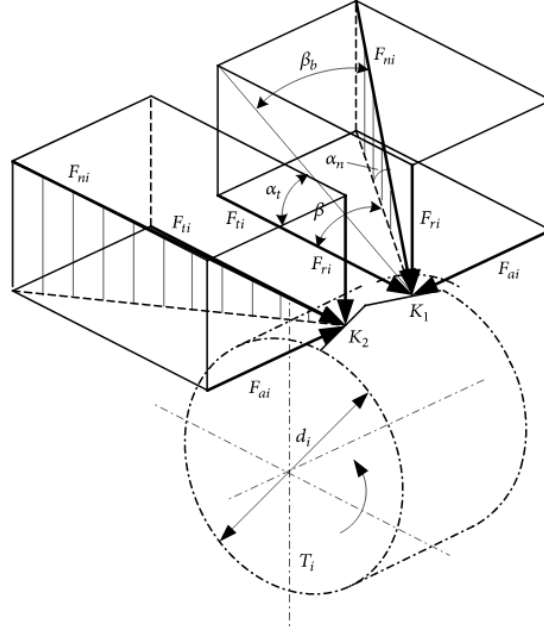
Fuerzas soportadas por un diente helicoidal al engranar [11]
